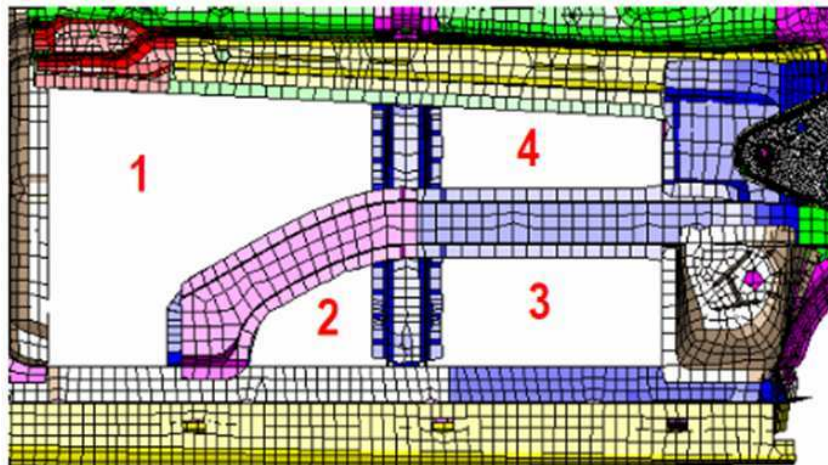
Découpage du plancher avant en sous-ensembles.
